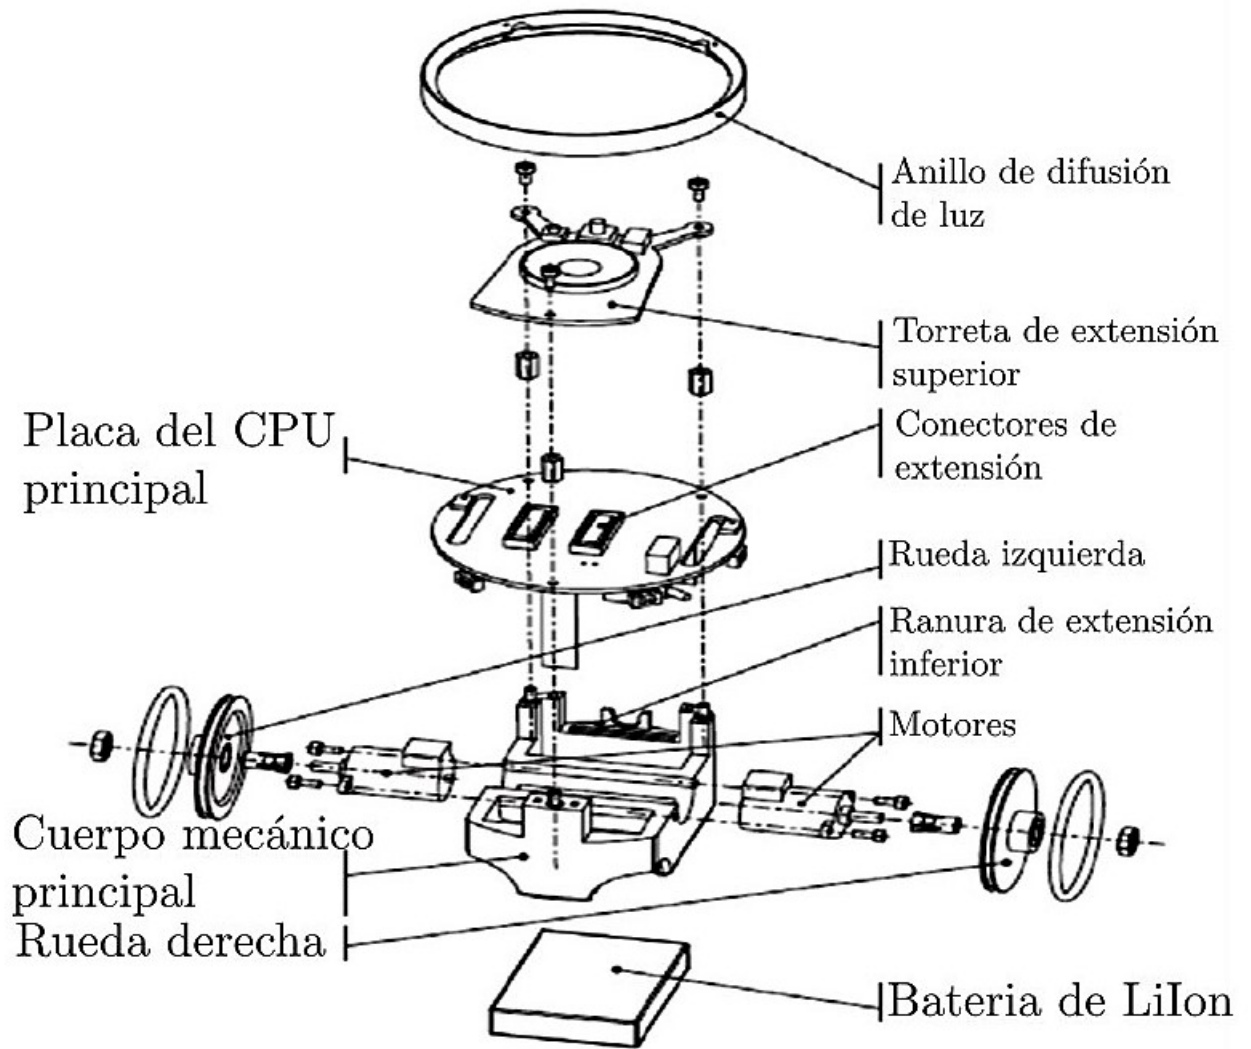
La estructura mecánica del robot e-puck en una vista explosionada.
